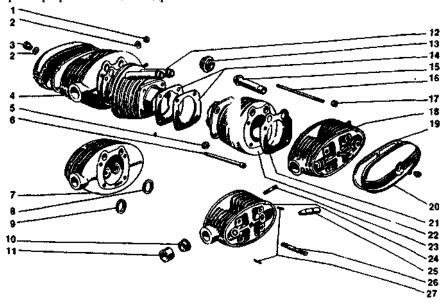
Цилиндры и головки цилиндров мотоциклов "Урал": 1 - гайка М8х1 (4 шт.); 2 - шайба 8 (6 шт.); 3 - гайка крепления крышки головки (2 шт.); 4 - головка правого цилиндра с клапанами в сборе; 5 - гайка М1 Ох I (8 шт.); 6 - трубка цилиндра сливная (2 шт.); 7 - головка правого цилиндра в сборе; 8 - седло впускного клапана (2 шт.); 9 - седло выпускного клапана (2 шт.); 10 - шайба патрубка (2 шт.); 11 - патрубок головки цилиндра (2 шт.); 12 - цилиндра в сборе (2 шт.); 13 - колпачок уплотнительный (4 шт.); 14 - прокладки цилиндра (2 шт.); 15 - кожух штанги в сборе (4 шт.); 16 - шпилька крепления головки цилиндра (8 шт.); 17 - гайка М8х1 (8 шт.); 18 - головка певого цилиндра с клапанами в сборе; 19 - прокладка крышки головки (2 шт.); 20 - крышка головки (2 шт.); 21 - прокладка головки цилиндра (2 шт.); 22 - цилиндр (2 шт.); 23 - шпилька М8х1х21 (4 шт.); 24 - головка левого цилиндра в сборе; 25 - направляющая клапана (4 шт.); 26 - шпилька М8х1х55 (2 шт.); 27 - штифт 4х12 (4 шт.)
